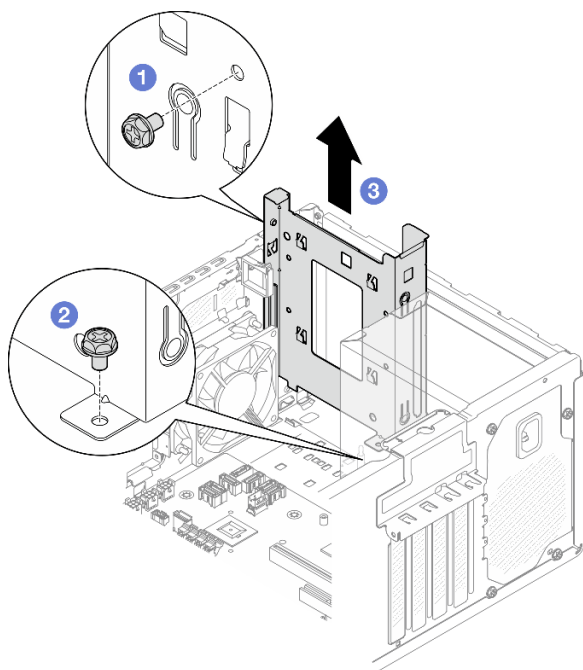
Entfernen der Laufwerkhalterung aus Laufwerkposition 0
